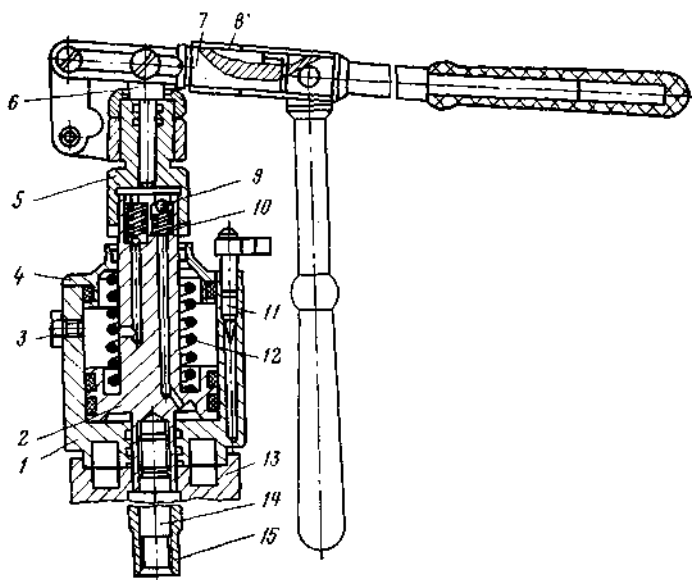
Малогабаритный пресс для продавливания отверстий в листовом металле
